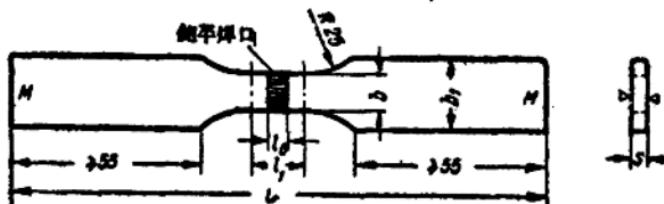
焊接接头破裂試驗用試样的形狀和尺寸
